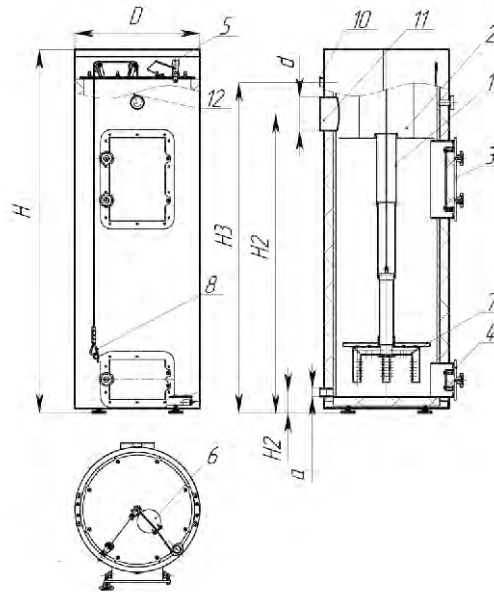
Габаритные и присоединительные размеры версии Comfort-XX (1 – телескопическая труба подачи воздуха, 2 – камера подогрева воздуха, 3 – проем для загрузки дров, 4 – проем для удаления золы, 5 – терморегулятор, 6 – устройство для регулирования подачи воздуха, 7 – распределитель воздуха, 8 – трос, 10 – патрубок подачи воды, 11 – дымоход для отвода дымовых газов, 12 – термоманометр).
